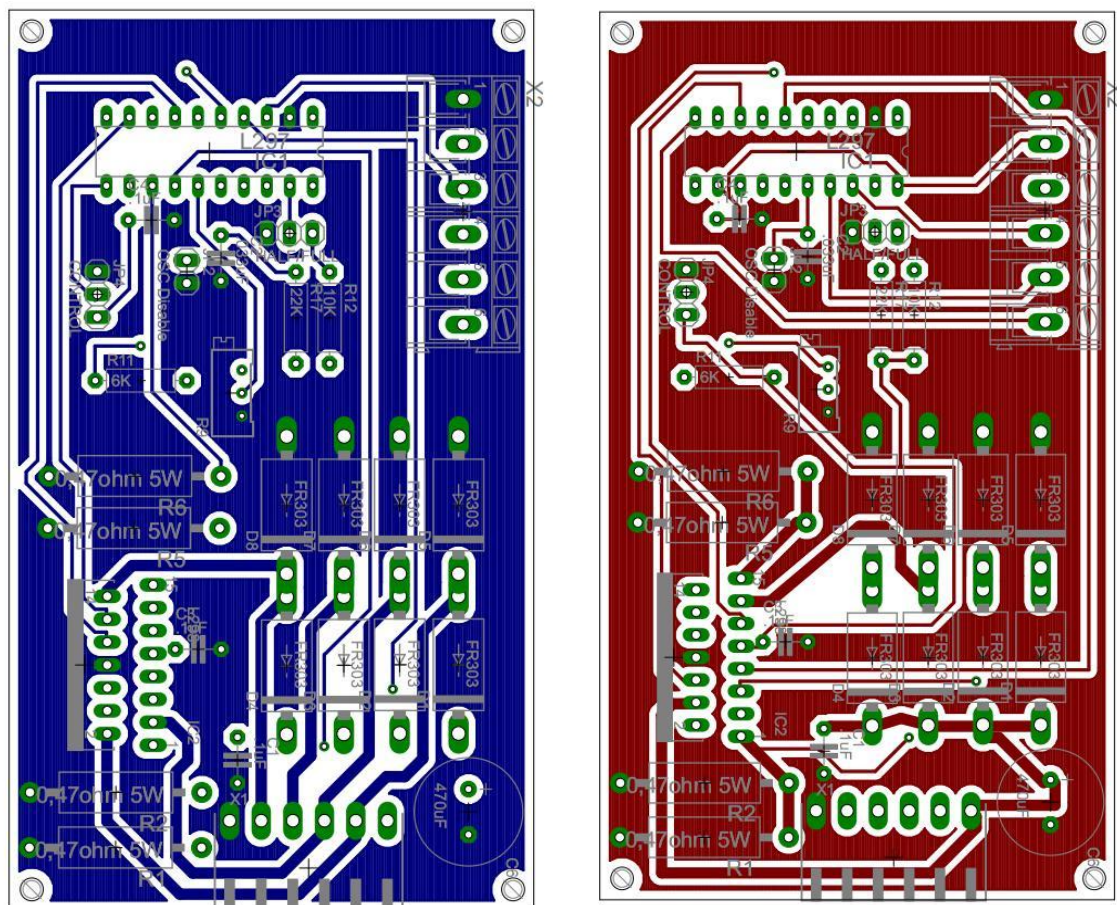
Layout del circuito impreso desarrollado para SIMVENT como controlador de motor tijereta. Izquierda capa inferior, derecha capa superior
